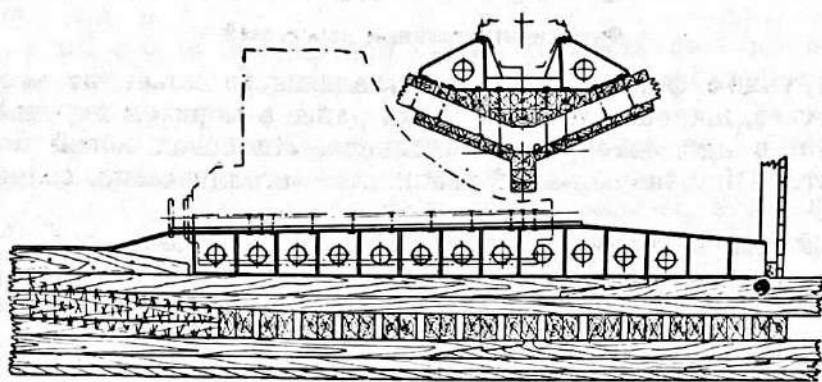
Сварной фундамент под двигатель 300 л. с. (1-й вариант).
